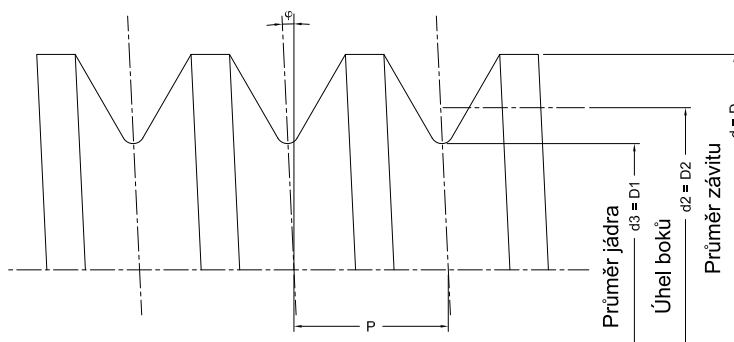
Pravý závit se šroubem stroje otáčejícím se doprava
